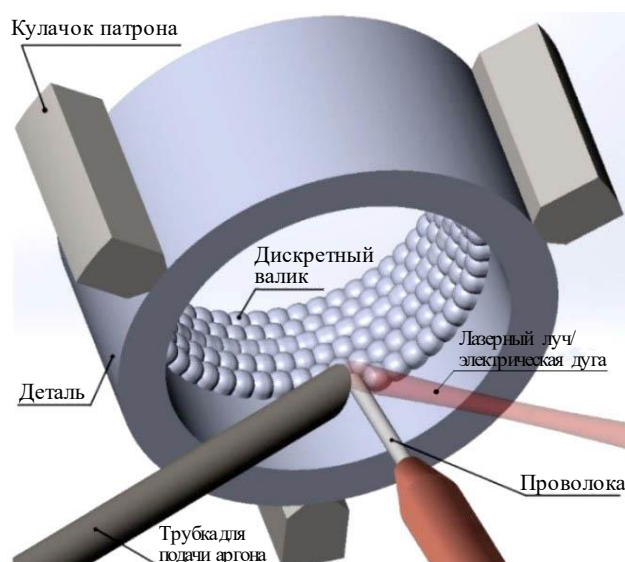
Схема лазерной и аргоно-дуговой наплавки конструктивно-подобного образца (втулки) из алюминиевого сплава АД33
